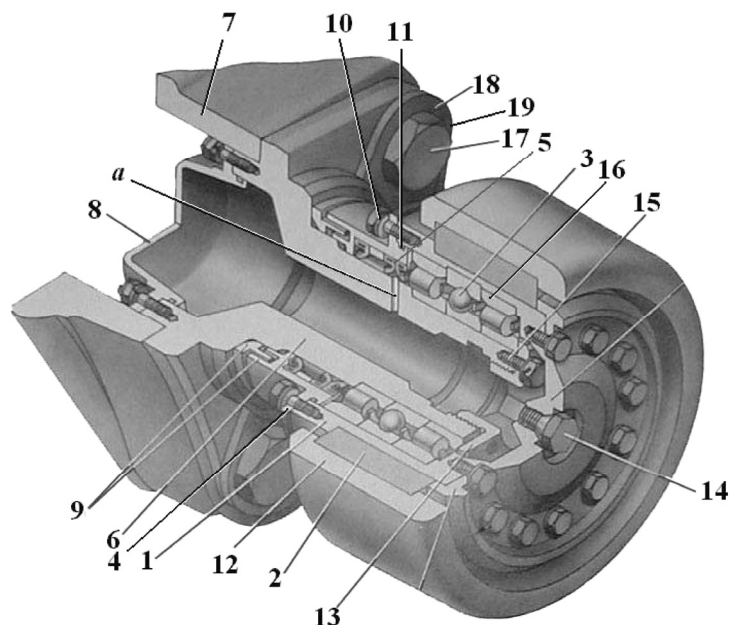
Поддерживающий каток: 1 – ступица; 2 – шина; 3 – шарикоподшипник; 4 – уплотнительная крышка; 5 – манжета; 6 – кронштейн; 7 – корпус танка; 8 – крышка; 9 – лабиринтное кольцо; 10 – болт; 11 – резиновое кольцо; 12 – стальной обод; 13 – гайка; 14 – пробка; 15 – стопорный болт; 16 – ролик; 17 – болт; 18 – шайба; а – сверление
